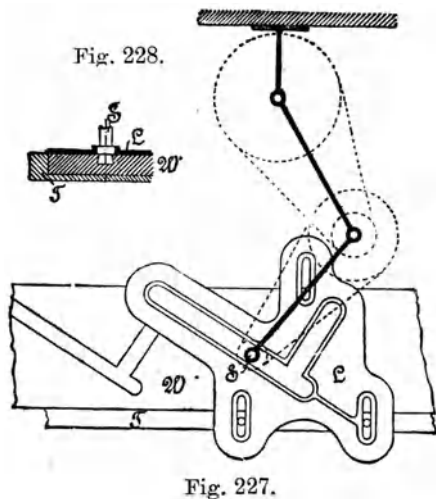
u. 228 erläutern ein Beispiel für das Einfräsen von Nuthen in eine ebene Fläche.<sup>1)</sup> Es ist Fig. 227 ein Grundriss der betreffenden Maschine und Fig. 228 ein Querschnitt durch Werkstück  $W$ , Lehre  $L$  und Maschinentisch  $T$ . Man verwendet als Maschine eine Langbein'sche Bohrmaschine (Bd. I, S. 379, Fig. 727). An einer Wand ist der mit Gelenk versehene Ausleger um eine lothrechte Axe schwenkbar gelagert. Er enthält in seinem äussersten Ende die Lager für den lothrechten Fräser  $S$ . Das Werkstück  $W$ , im vorliegenden Falle eine Treppenwange, ist auf den Tisch  $T$  gelegt und über ihm die Lehre  $L$  befestigt. In den Schlitz dieser Lehre findet nun der Hals des Fräasers oder Langlochbohrers die verlangte Führung, während seine Verschiebung mittels der Hand stattfindet. Dieser von Perry angegebenen Einrichtung ist eine andere, von J. Royle & Sohn,<sup>2)</sup> sehr nahe verwandt. Man kann sie selbstverständlich für jede beliebige Gestalt solcher Nuthen anwenden, so lange der kleinste Krümmungshalbmesser der Seitenflächen nicht kleiner ist als der Fräserhalbmesser.
